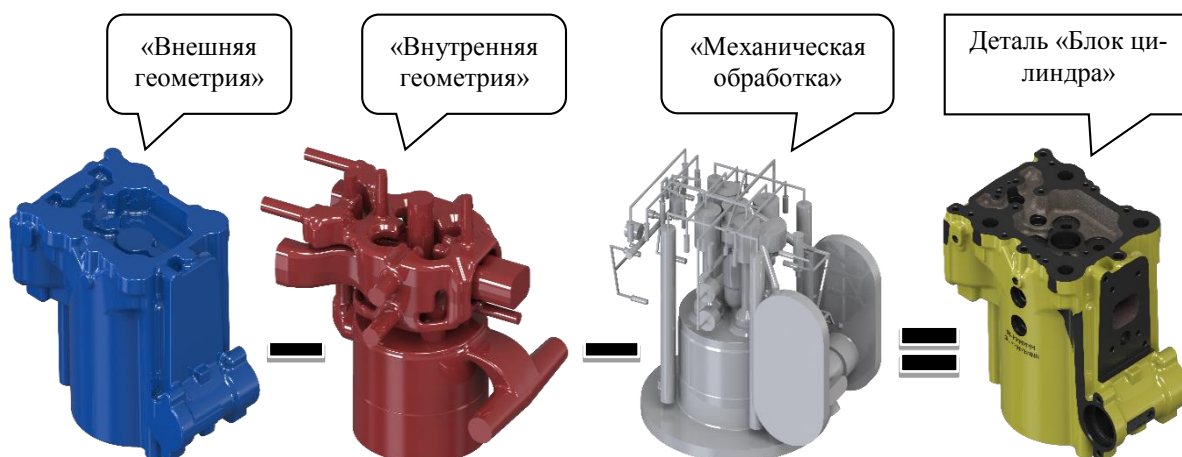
Компоновка модели детали «Блок цилиндра»
